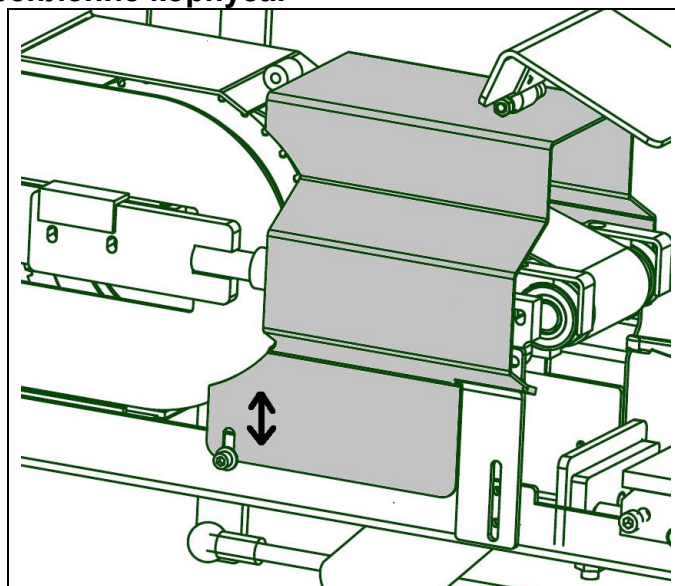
Корпус демонтируется отпусанием двух болтов.
